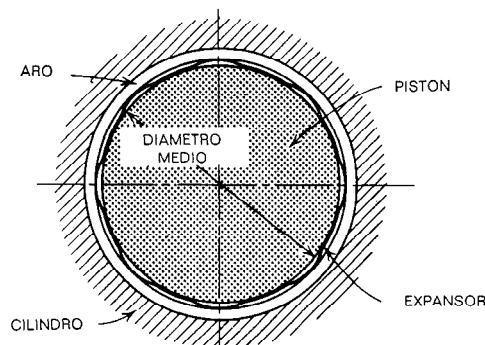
Posición del expansor en el interior del aro (Muskegon Piston Ring Company).
